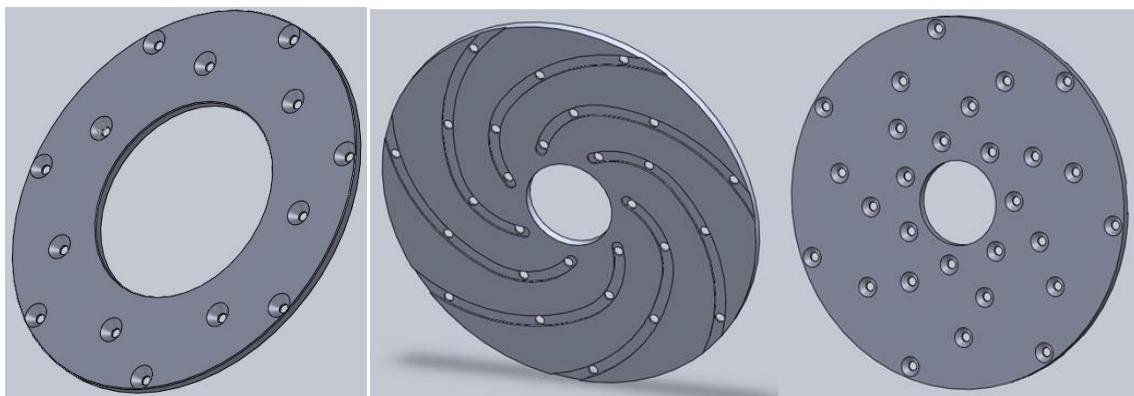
3D model rotora centrifugalne pumpe u lijevanoj izvedbi
